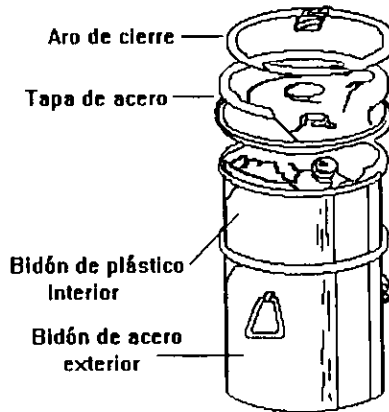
f) Bidón de plástico reforzado con protección exterior de acero con reborde discontinuo.
